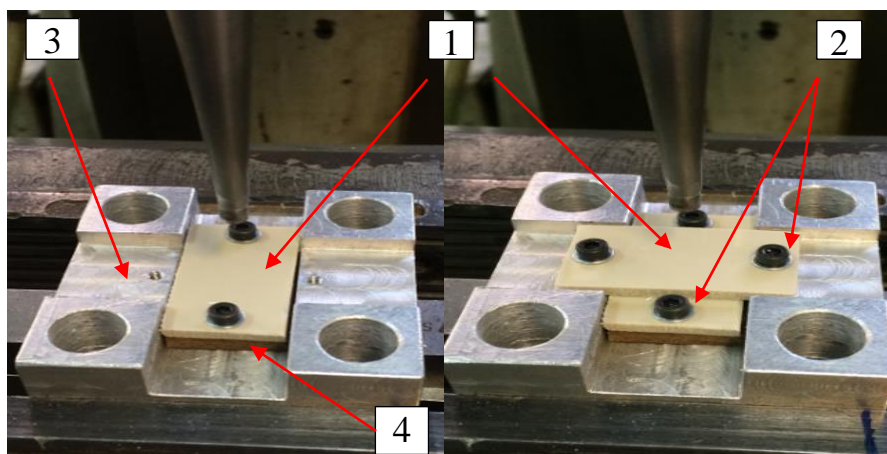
Оснастка для фиксации плоских образцов при сварке
